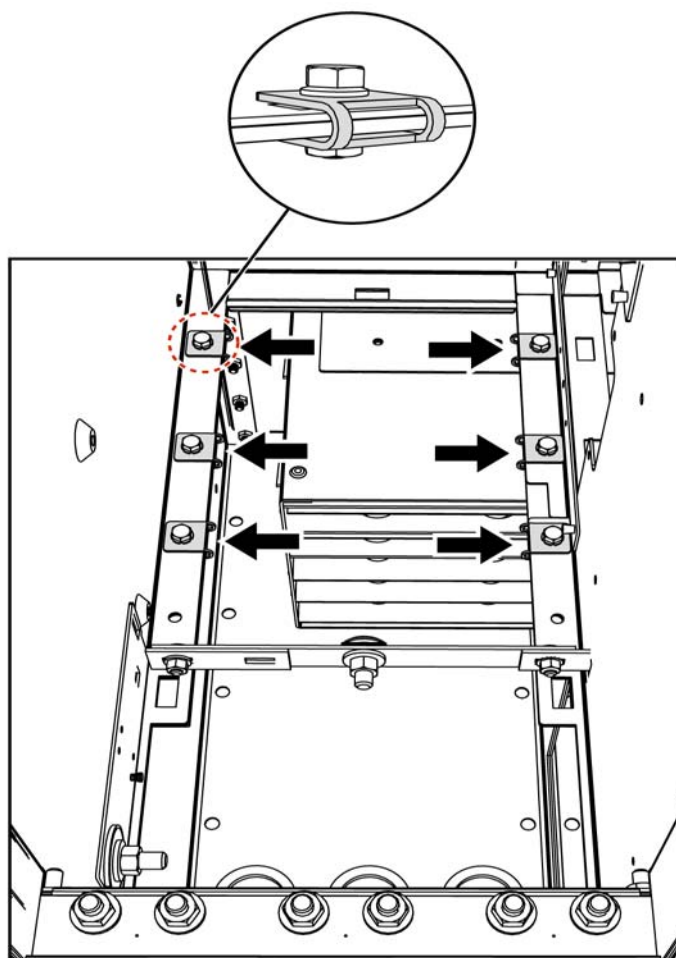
Точки соединения РУ - цоколь (вид спереди в кабельный блок)
